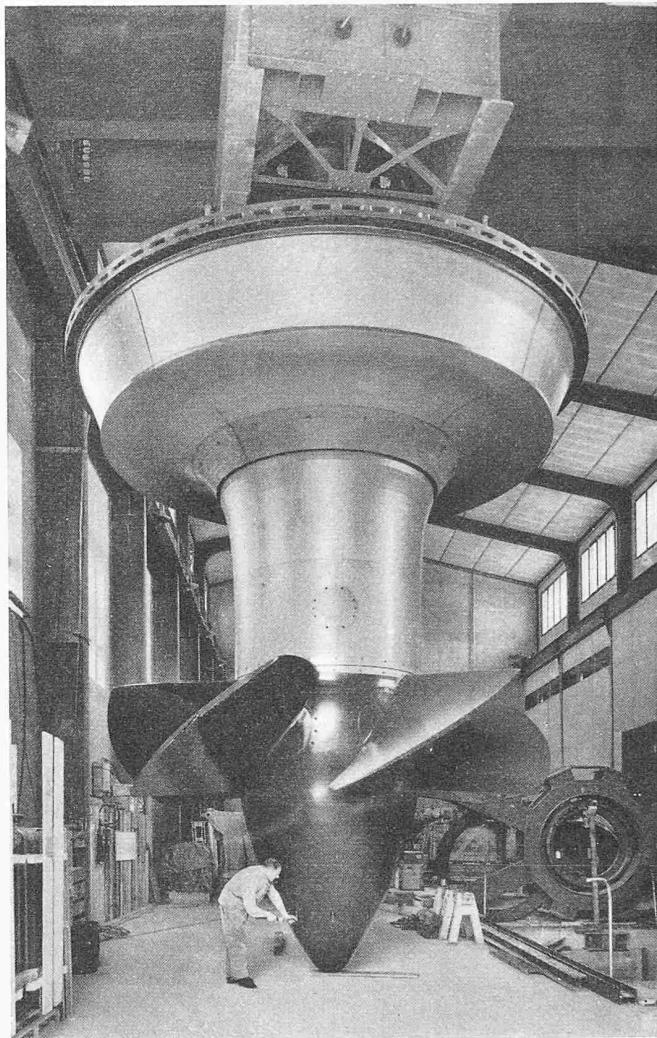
(oben). Laufrad mit Lagermantel und Turbinendeckel von dem Einbau im Maschinenhaus. 21. April 1952
